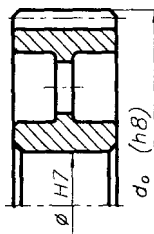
Представление отклонений размеров заготовки для диаметров вершин зубьев
